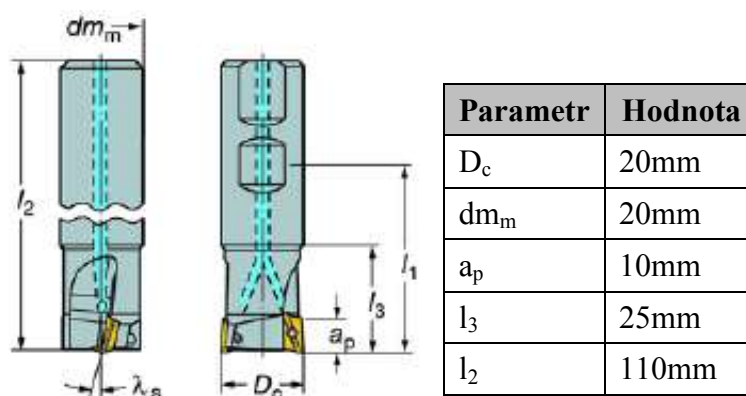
VBD - R390-11 T3 08M-MM 2030 [11].
